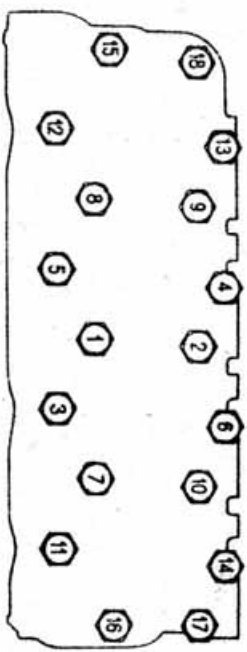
Порядок подтяжки гаек крепления головки цилиндров.
